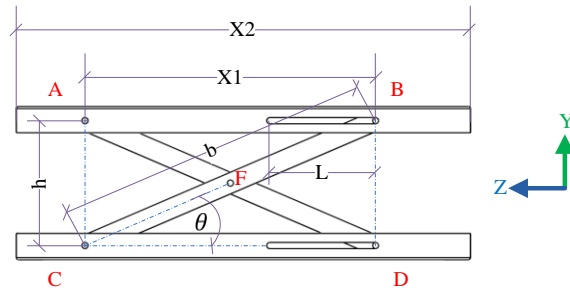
Dimensiones principales del mecanismo tipo tijeras.
